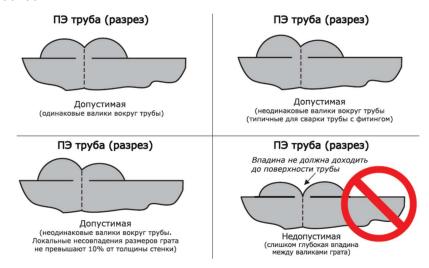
Виды грата при сварке нагретым инструментом
